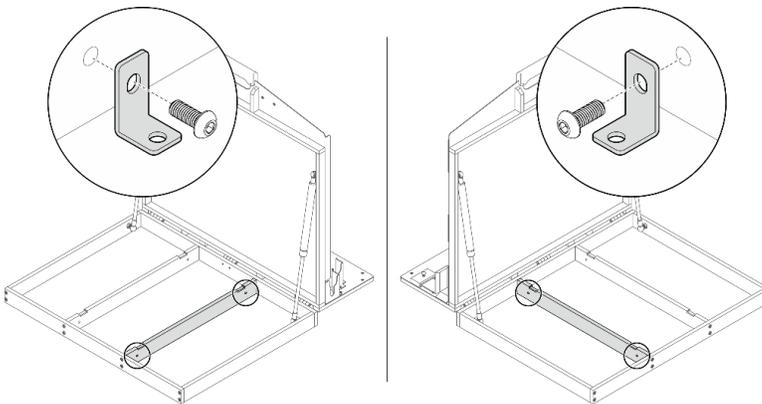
Installation des pattes de fixation en forme de L sur le dispositif rotatif
